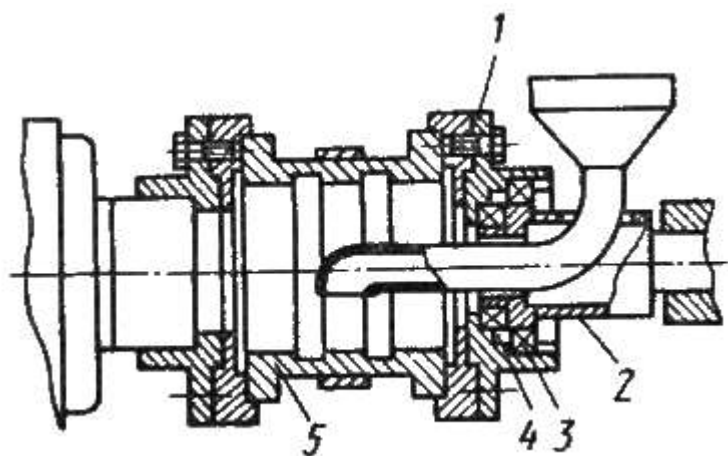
Приспособление для центробежной заливки подшипников скольжения: 1 — вращающаяся крышка; 2 — неподвижная оправка; 3 — радиальный подшипник; 4 — упорный подшипник; 5 — вкладыш.
